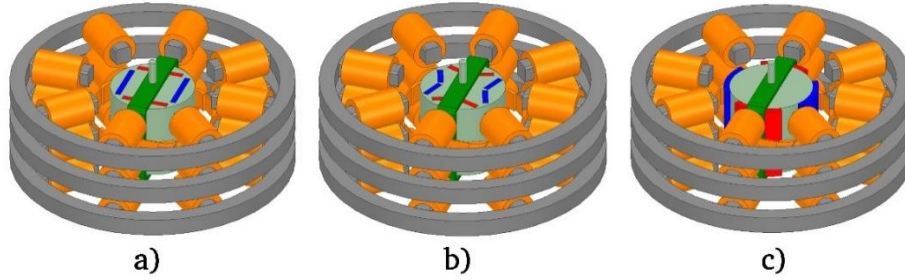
SMKM1 ve SMKM2 motor modellerinin dış gövdesi
